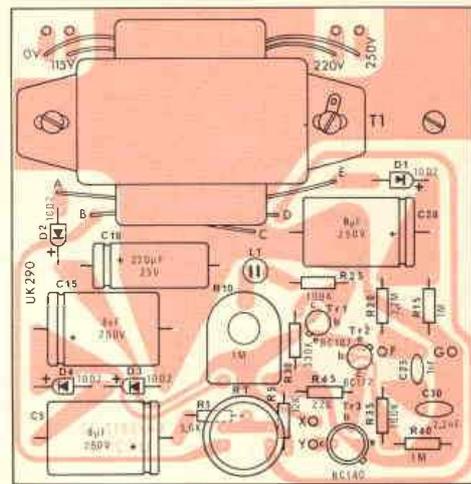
Montaggio dei componenti sul circuito stampato.
